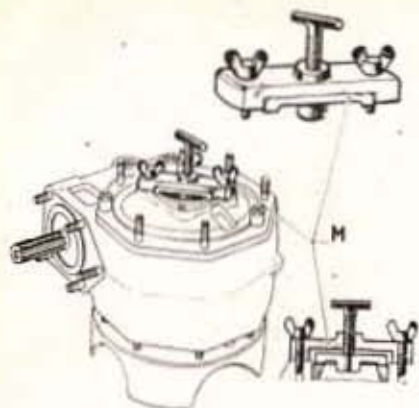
La bride (M) appuie la bague extérieure du roulement sur l'anneau de galets côté D.
